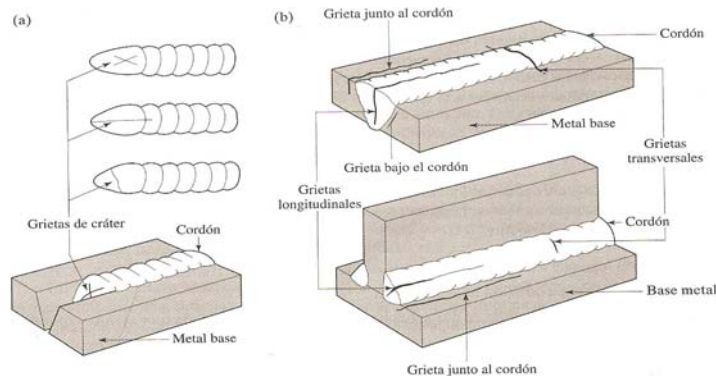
Tipos de grietas en uniones soldadas, debidas a esfuerzos térmicos que se desarrollan durante la solidificación y la contracción del cordón de soldadura y la estructura que la rodea. (a) Grietas de cráter. (b) Varios tipos de grietas en uniones a tope y en T
